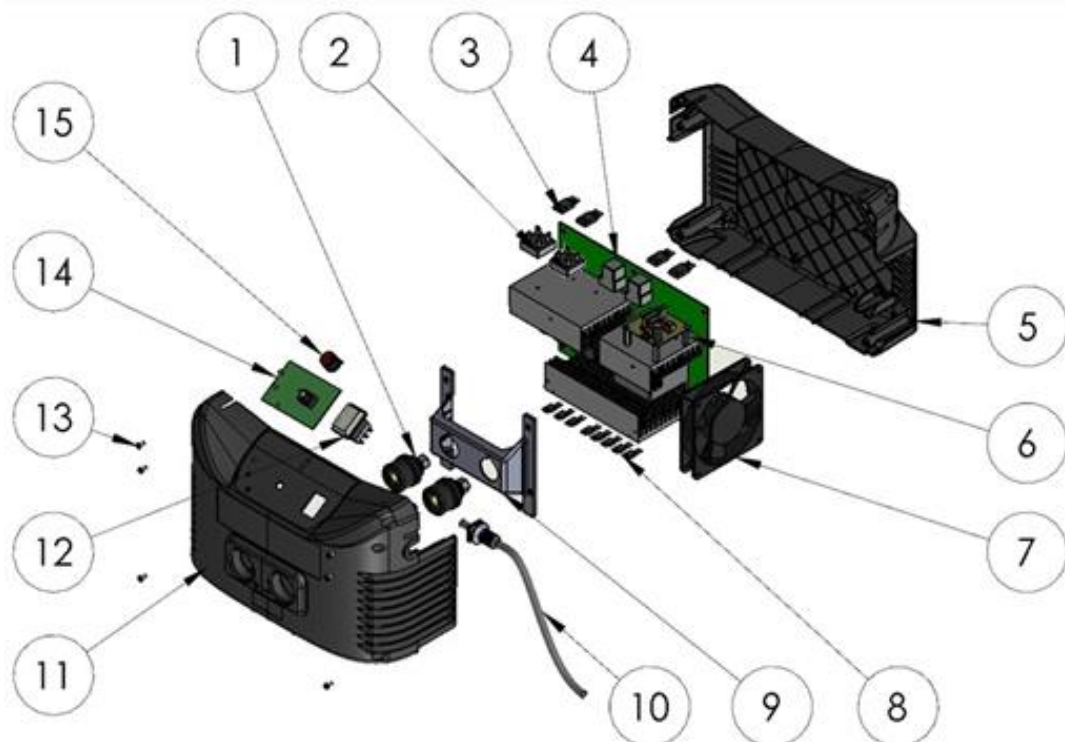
Vista explodida Vulcano Inverter 200 DV
